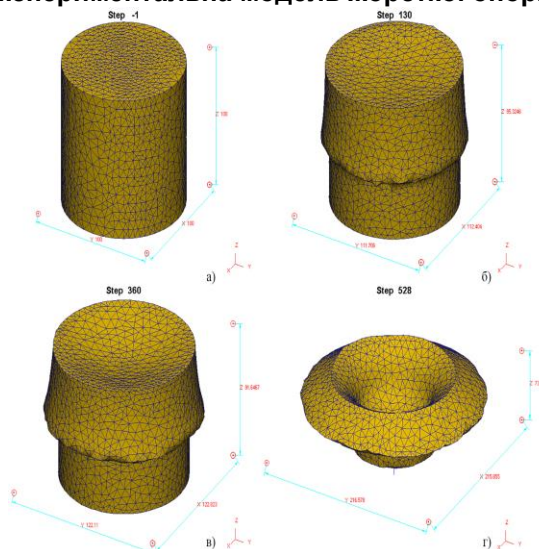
Формозміна циліндричної заготовки при ШО: а) початковий етап; б) на 130 кроці ШО; в) на 360 кроці ШО; г) кінцевий крок деформування
